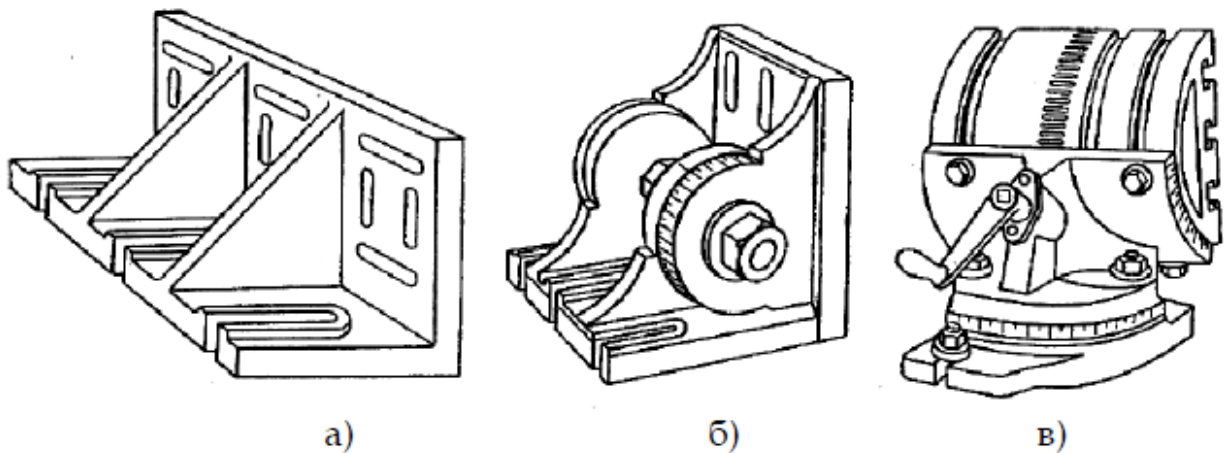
Закріплення заготовок на кутових плитах і призмах
